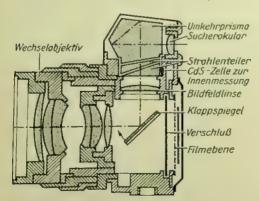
Schnitt durch eine einäugige Spiegelreflexkamera
